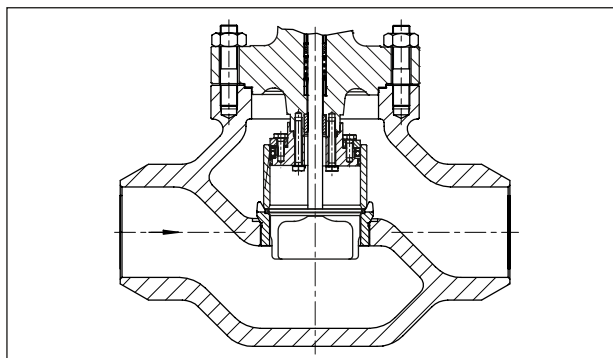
Ventil Typ 3251/3251-AM mit Anschweißenden und druckentlastetem Ventilkegel
